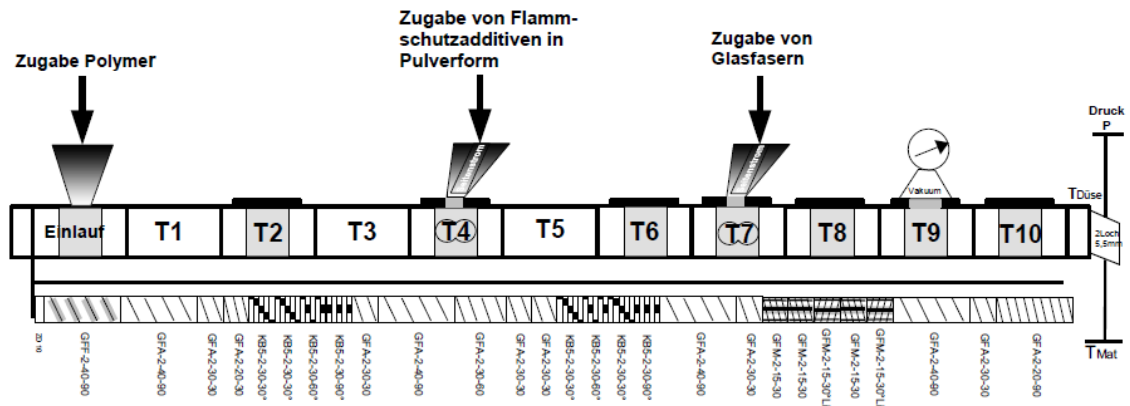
SK I, ZSE 27, für PA6 und PA66, 1. Extrusionsstufe (Compoundierung).
